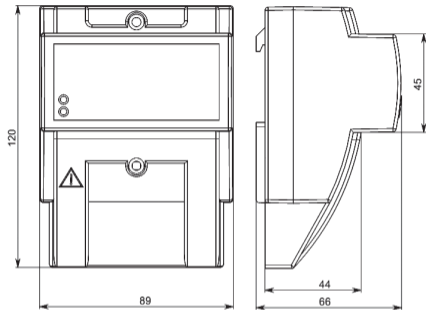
Счетчики в корпусе W1 для установки на щиток
